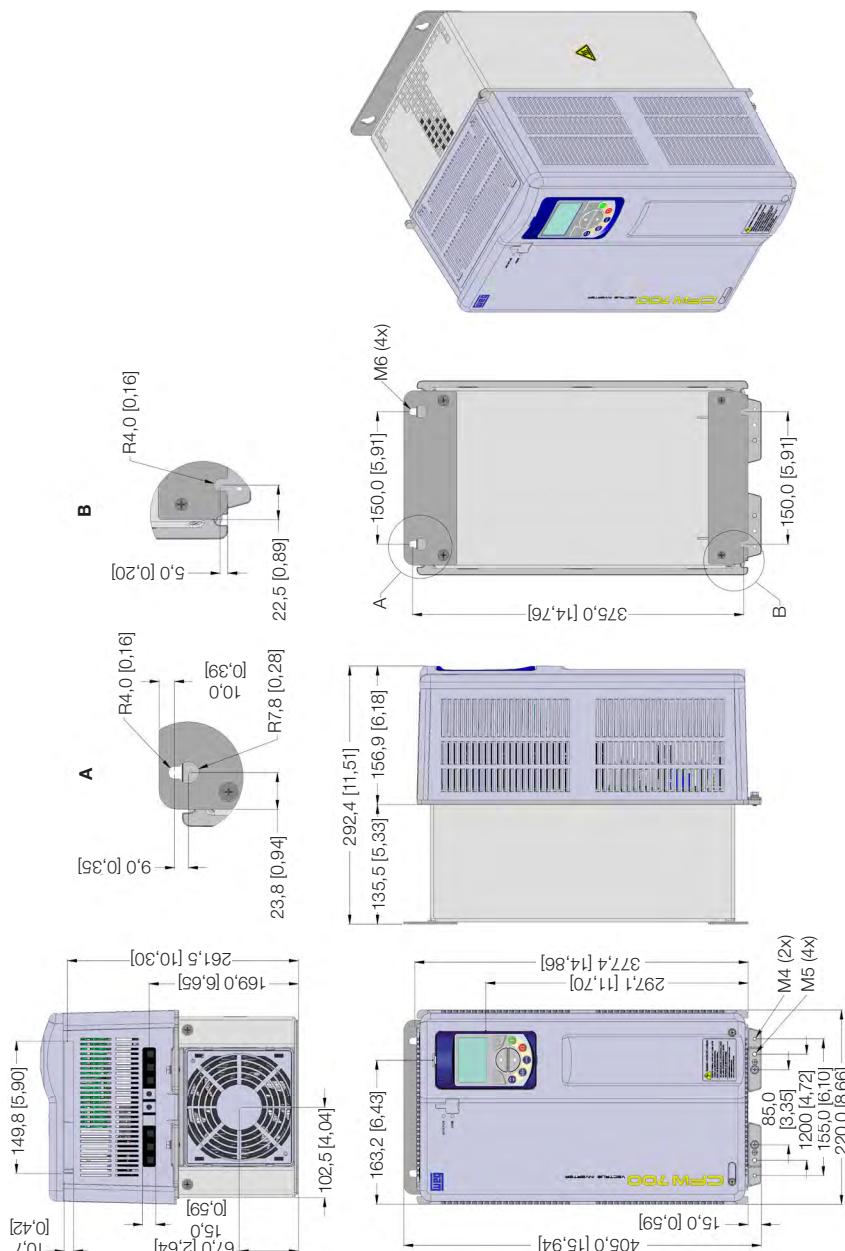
Umrichterbaugröße in mm [-in] - gehäuse C
